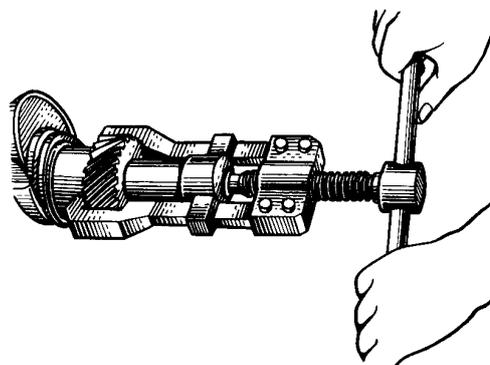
Демонтаж шестерни с коленчатого вала с помощью съемника мод. 1П-21305
